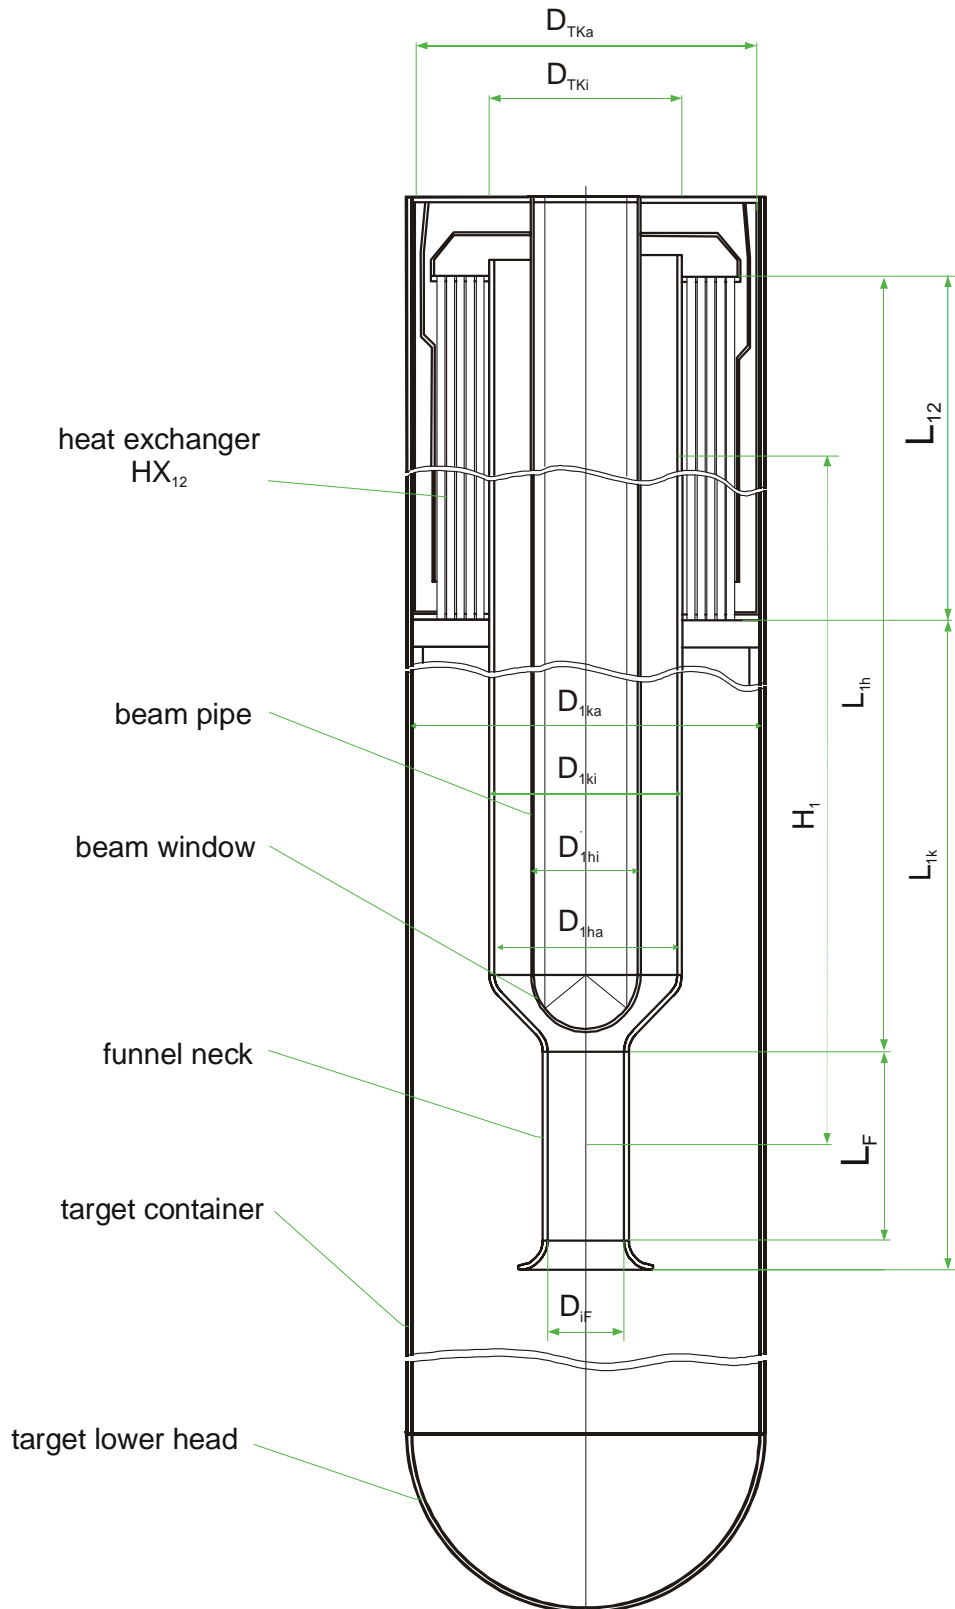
Schematische Darstellung des geschlossenen Spallationstargets mit Spallationsbereich, Strahlfenster und Primär-Sekundär-Wärmetauscher mit den wichtigsten Bezeichnungen.
